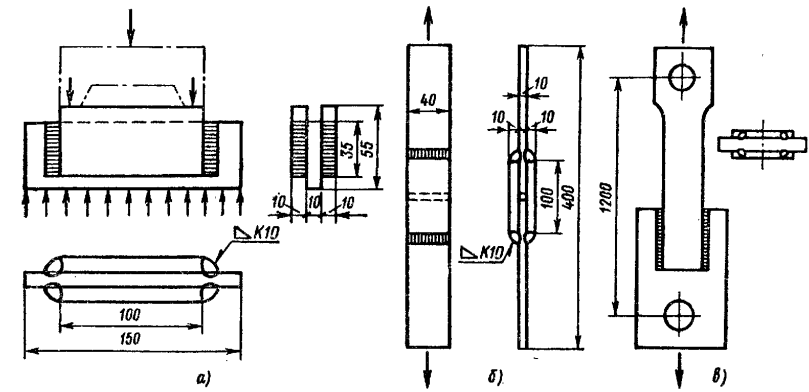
Образцы для испытаний на срез фланговых (а, в) и лобовых (б) швов и схемы приложения нагрузки к образцам
